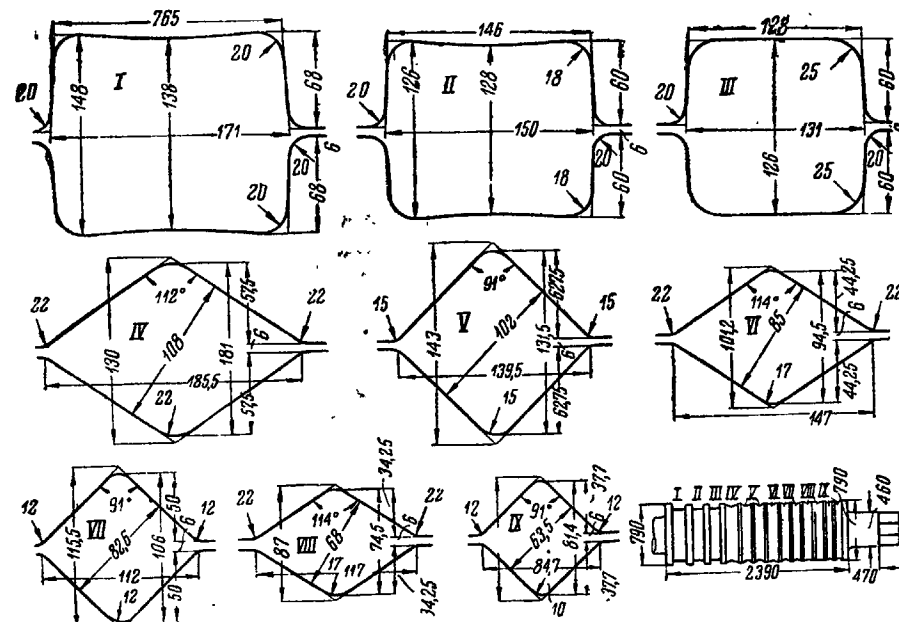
Калибровка валков дуо-реверсивного стана для заготовок
